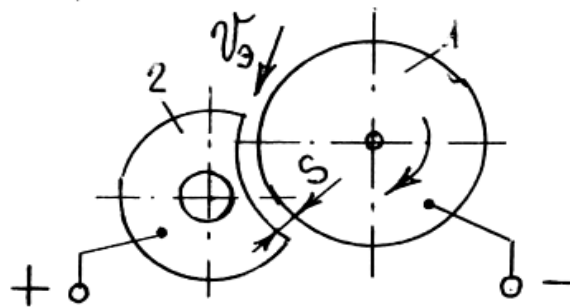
Схема розрізання профільованим інструментом: 1 – електрод-інструмент (диск); 2 – заготовка
